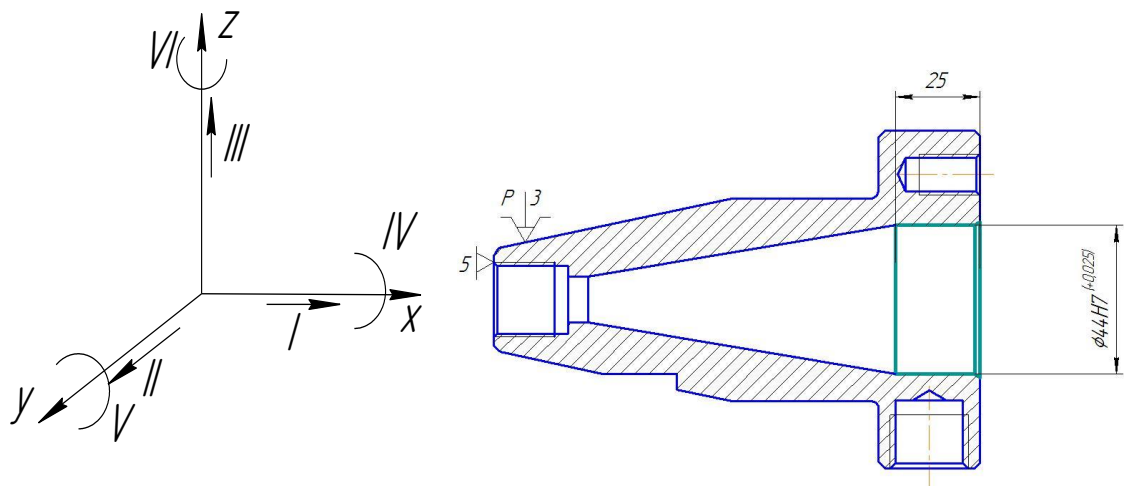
Ескіз обробки заготовки на операції 040
